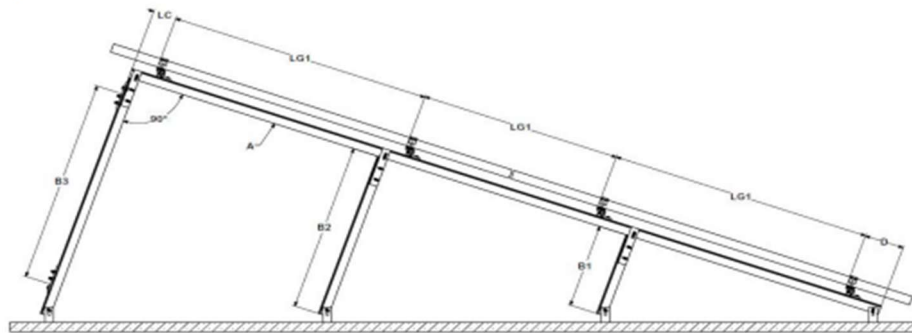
Dimensiones de ensamble para el sistema CrossRail Tilt-Up Multi-Row 1 Fila.
